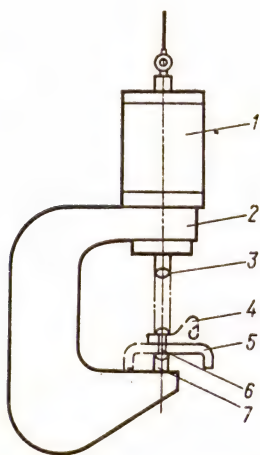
Переносная клепальная установка (скоба) для клепки автомобильных рам: 1 — рабочий цилиндр; 2 — скоба; 3 и 7 — соответственно подвижный и неподвижный бойки; 4 — кронштейн; 5 — продольная балка рамы; 6 — заклепка
